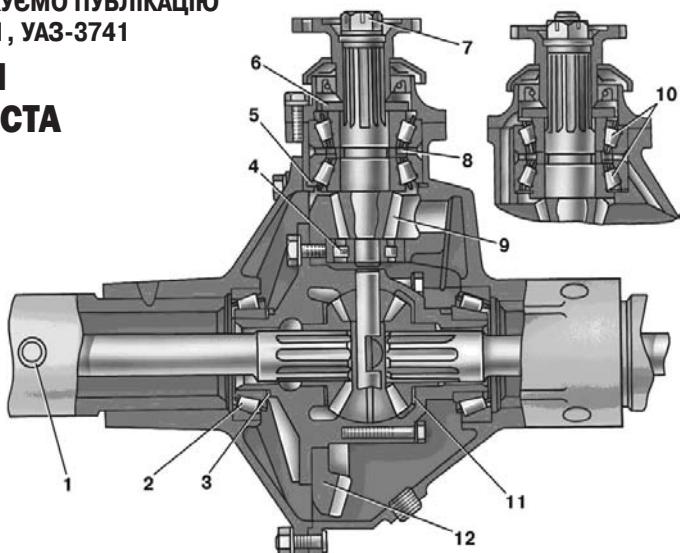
Задній міст: 1 – запобіжний клапан; 2 – підшипник диференціала; 3, 8 – регулювальні прокладки; 4 – задній підшипник ведучої шестерні; 5* – регулювальне кільце; 6 – маслозгінне кільце; 7 – гайка; 9 – ведуча шестерня; 10 – передній підшипник ведучої шестерні; 11 – упорна шайба напівосьової шестерні; 12 – ведена шестерня. (* з 1991 р. не встановлюється)
